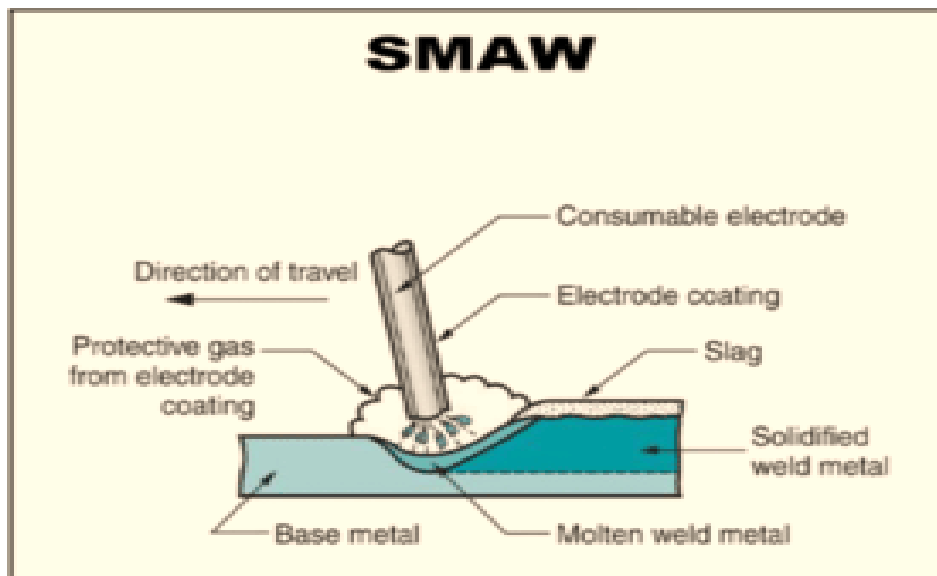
Principe de soudage à l'arc avec électrode enrobée (SMAW). [28]
